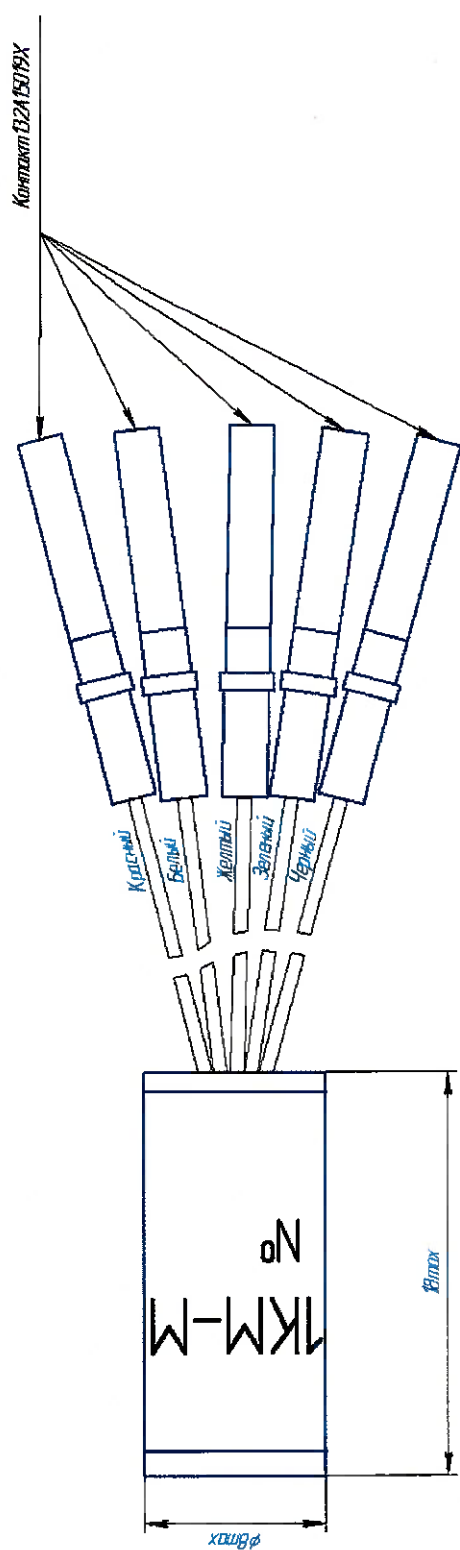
Габаритный чертеж КМ-М ТЮКН.467369.005
